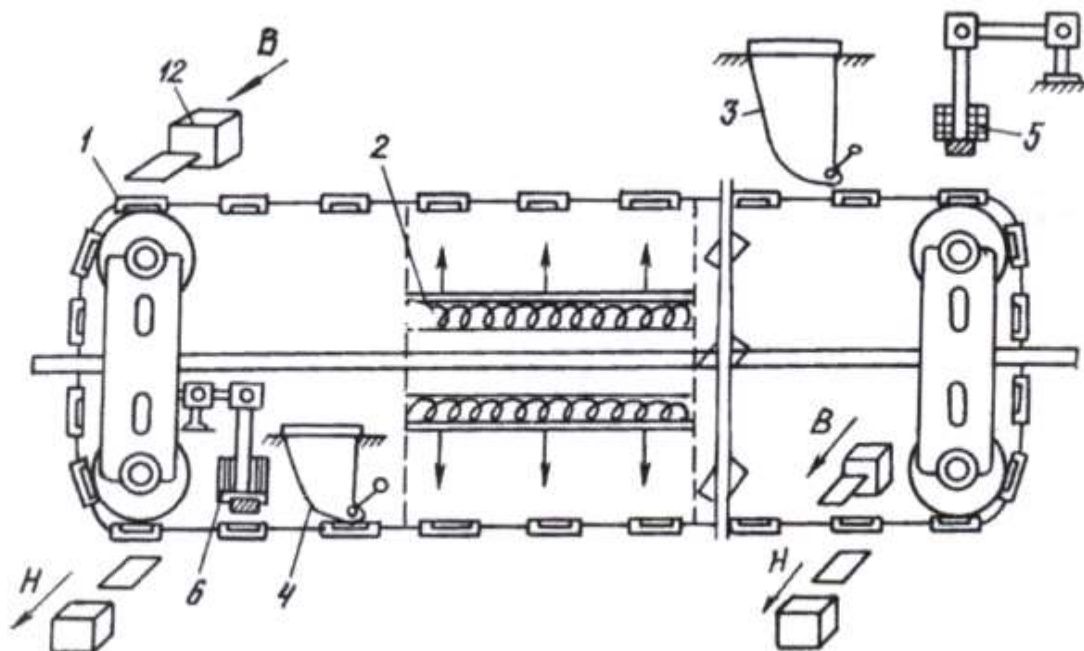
Устройство для выпечки хлебобулочных изделий с начинкой
